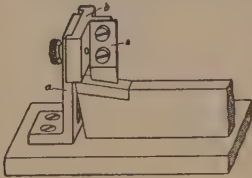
Soldadura de una plaquita ensamblada; c, cobre
